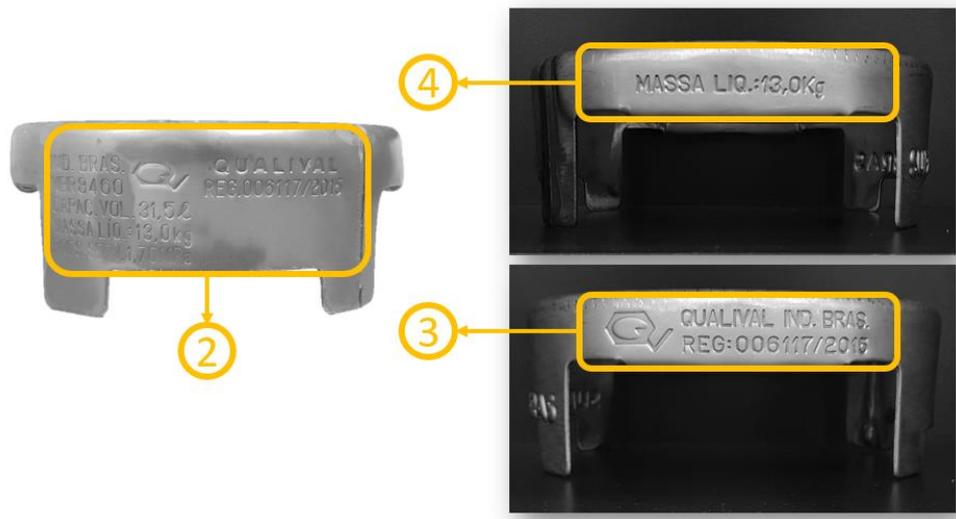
Estudo de novo layout para a gravação das Alças P13.
